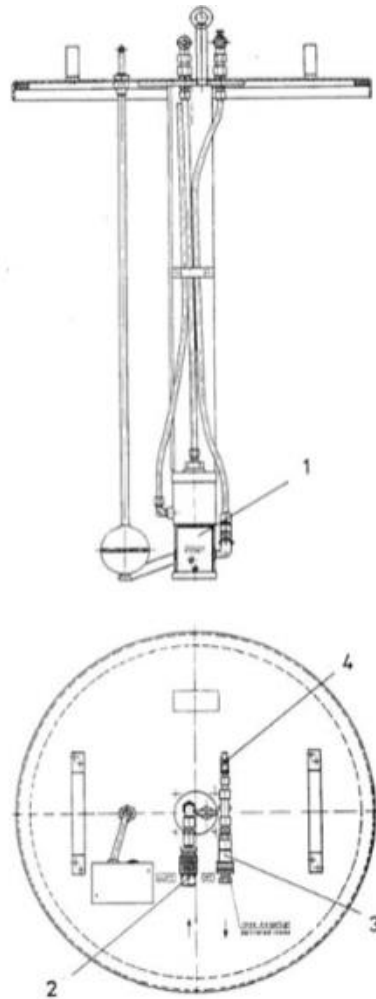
Alzado y planta de la bomba SAF2-YL.
